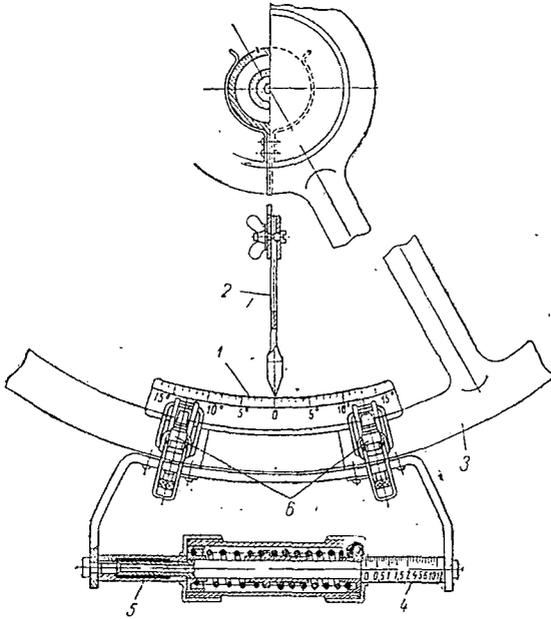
Прибор для проверки рулевых управлений грузовых автомобилей:
